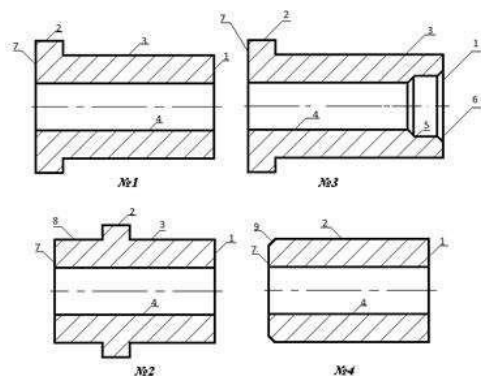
Группа деталей с нанесенными номерами поверхностей.
